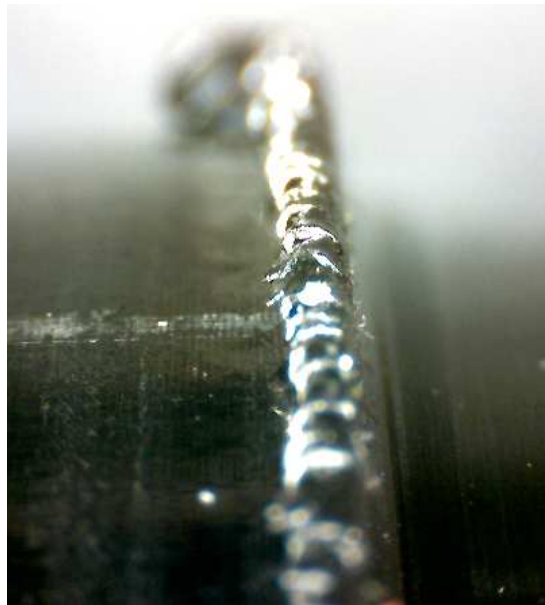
1- Corpo de prova com rebarba, após a usinagem de torneamento durante os ensaios de vida
